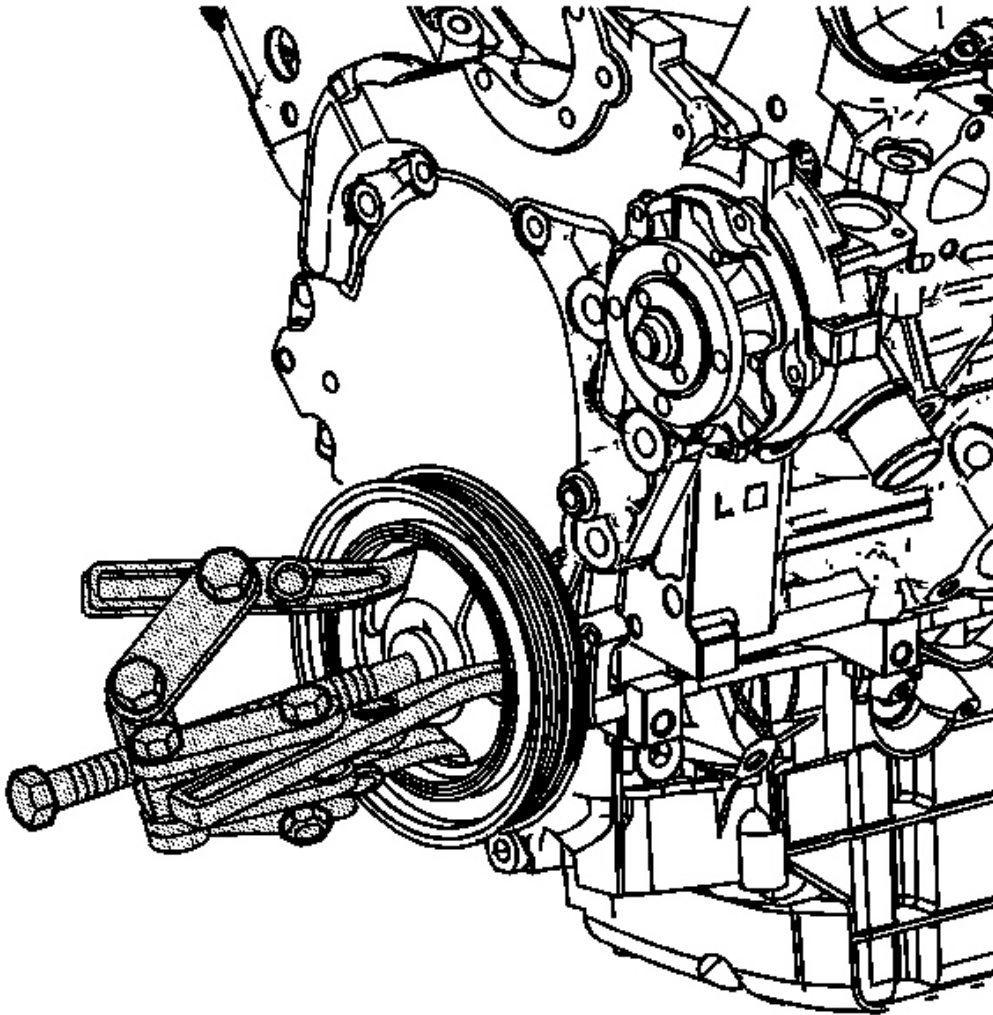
Vista del cigüeñal del balanceador, perno y arandela
